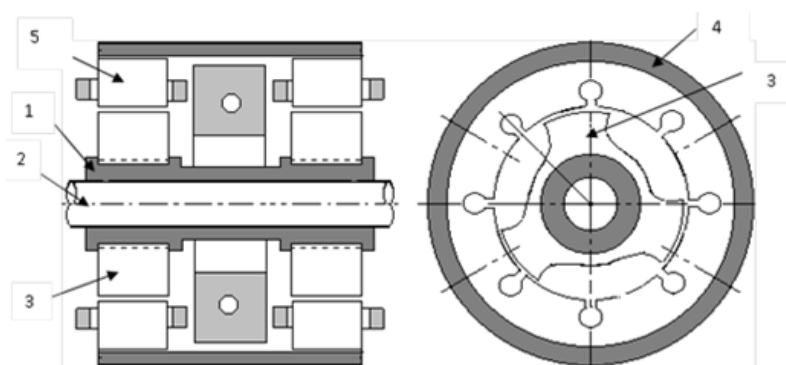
Двухпакетный индукторный генератор униполярного типа
